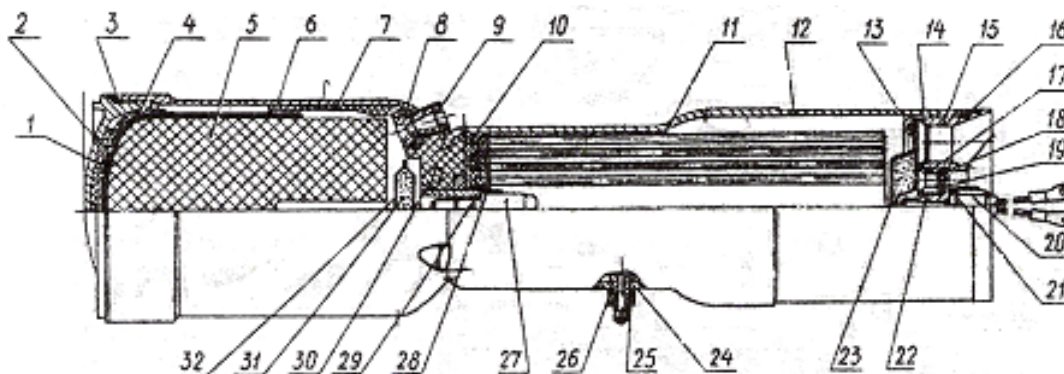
Твердотопливный двухрежимный ракетный двигатель: 1 – прокладка; 2 – крышка; 3 – кольцо уплотнительное; 4 – опора; 5 – заряд разгонно-маршевый; 6 – камера разгонно-маршевая; 7 – экран; 8 – вкладыш; 9 – заглушка; 10 – поддон; 11 – заряд стартовый; 12 – камера стартовая; 13 – винт; 14 – колпачок; 15 – блок сопловой; 16 – прокладка; 17 – вкладыш; 18 – кольцо; 19 – мембрана; 20 – электровоспламенитель; 21 – прокладка; 22 – ниппель; 23 – воспламенитель; 24 – штуцер; 25 – колпачок; 26 – кольцо; 27 – воспламенитель лучевой замедленного действия; 28 – гайка; 29 – прокладка; 30 – втулка; 31 – воспламенительный состав; 32 – воспламенитель
